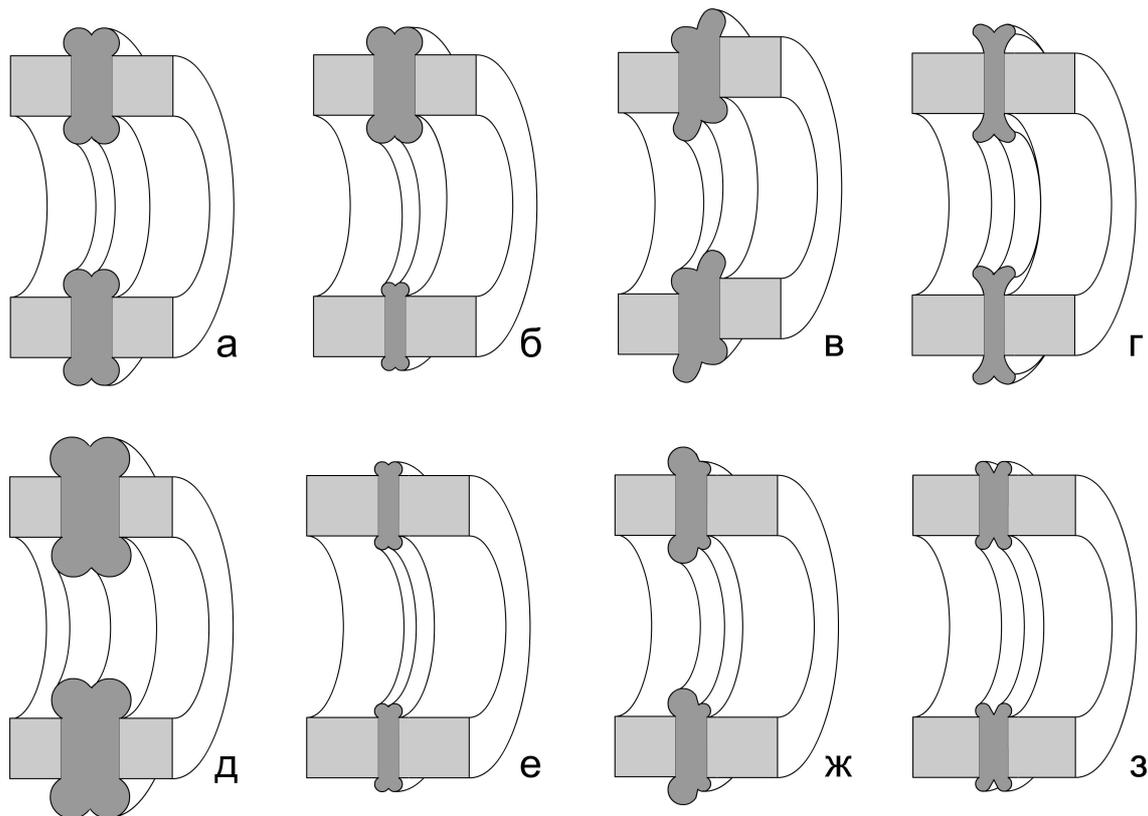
Типичные ошибки при стыковой сварке
